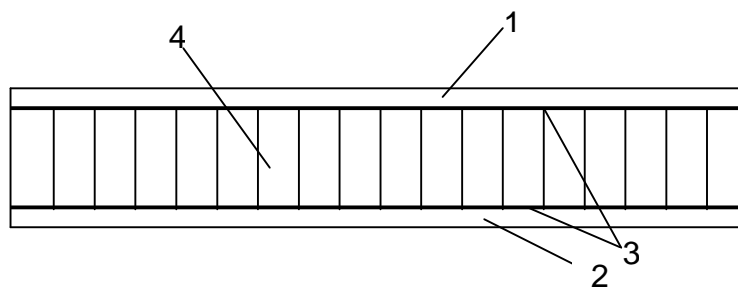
Фрагмент трехслойной конструкции ТИ для испытаний:
